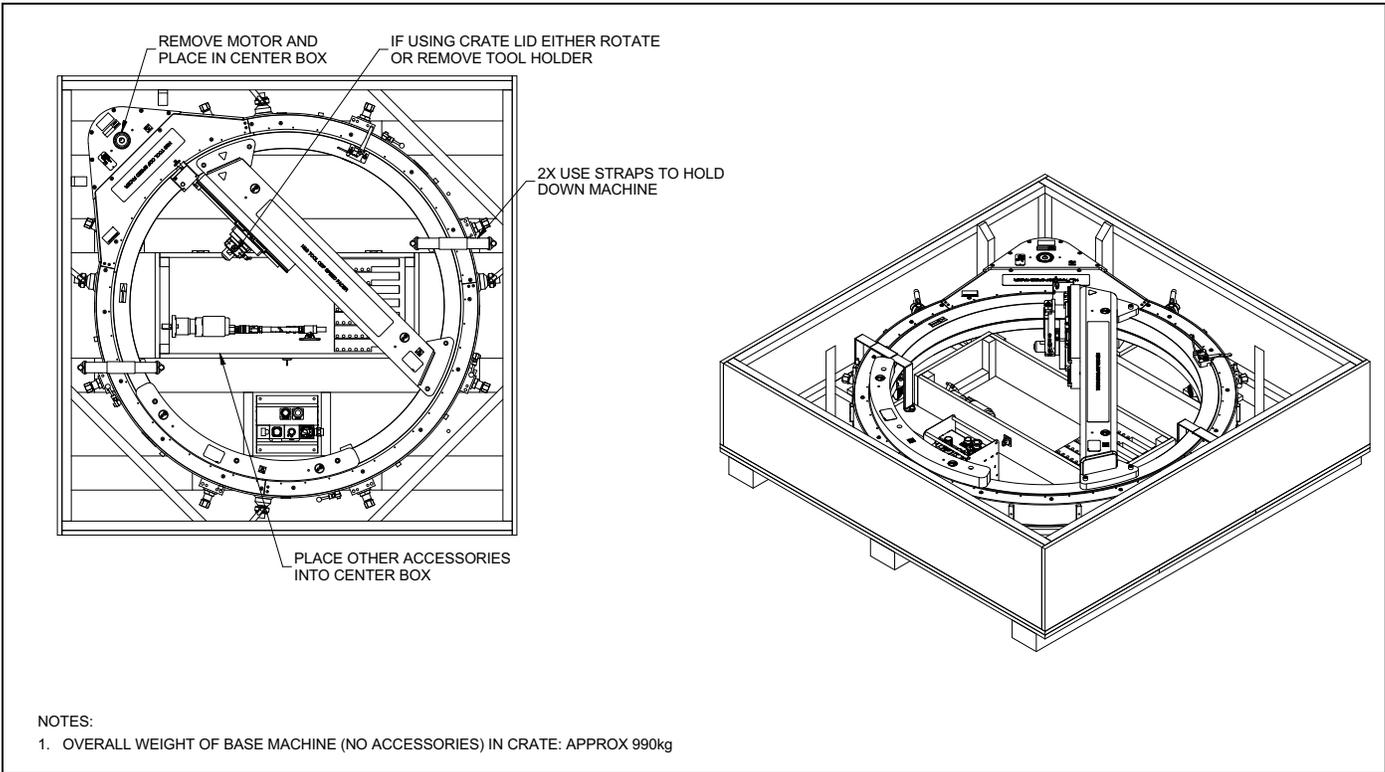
CAISSE D'EXPÉDITION DE LA MACHINE ODF50
